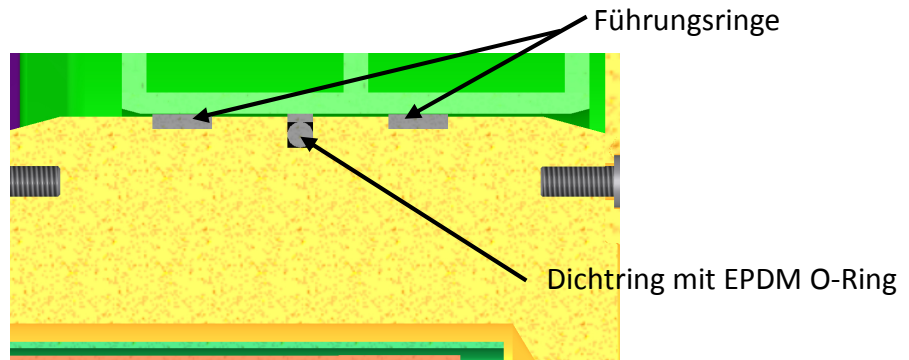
Kolbenstangendichtung mit Kolbenführung
